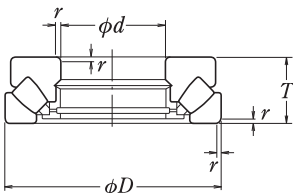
Rodamientos de Rodillos Esféricos de Empuje
